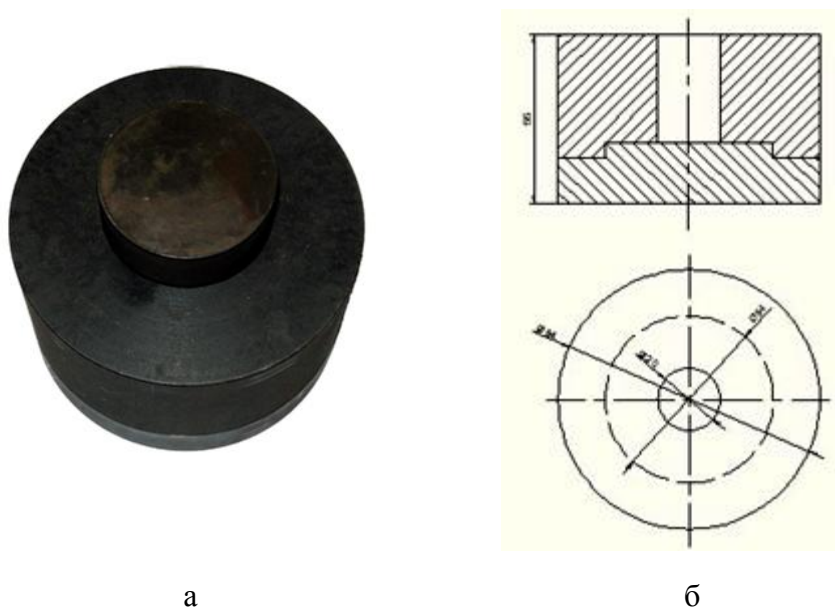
Общий вид (а) и сборочный чертеж (б) матрицы для изготовления опытных образцов
